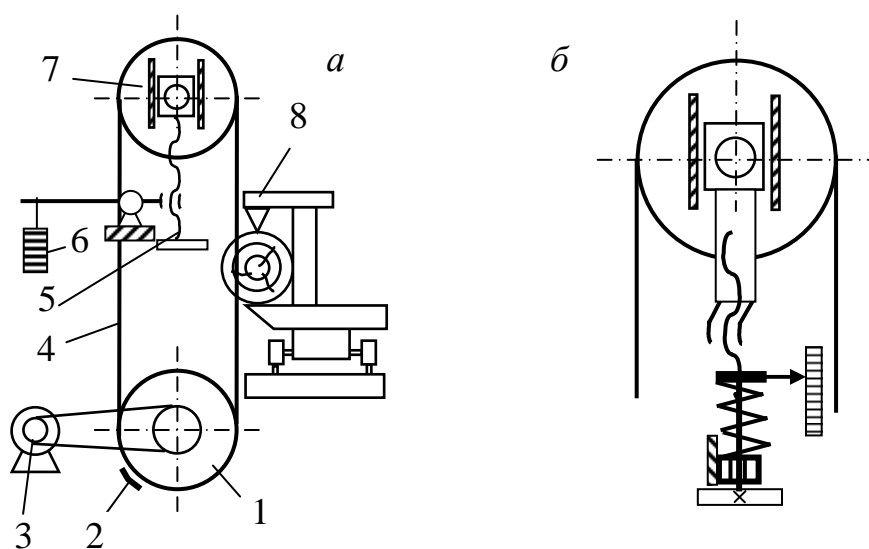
Механизмы главного движения ленточнопильных станков с натяжением пильной ленты:
